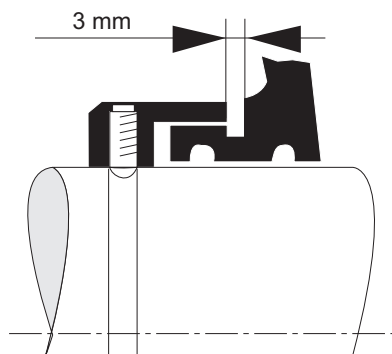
Расположение установочных винтов лабиринтного уплотнительного кольца на наружной крышке подшипника
